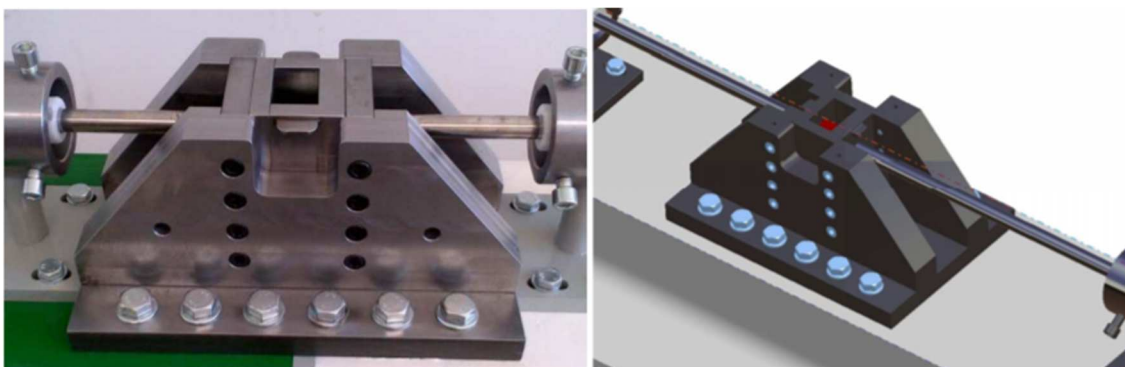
Sistema di arresto, componente reale in opera e CAD 3D.
